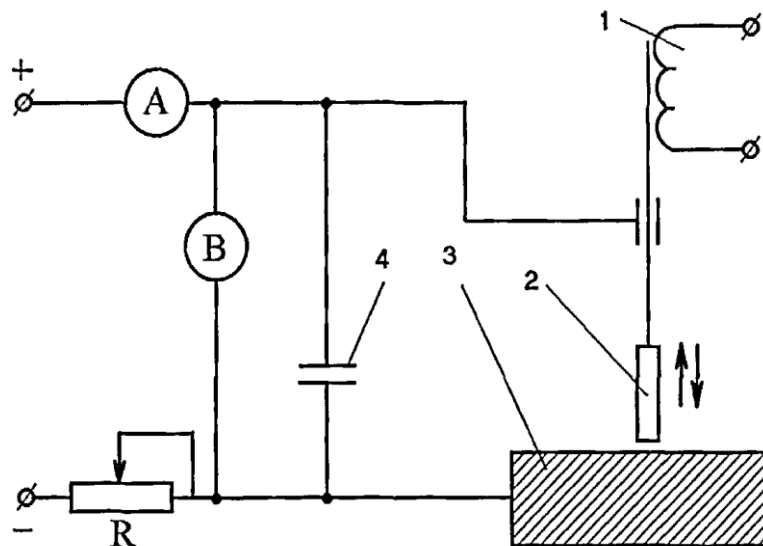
Схема установки для електроіскрової обробки: 1 – вібратор; 2 – інструмент (анод); 3 – деталь; 4 – конденсатор.
